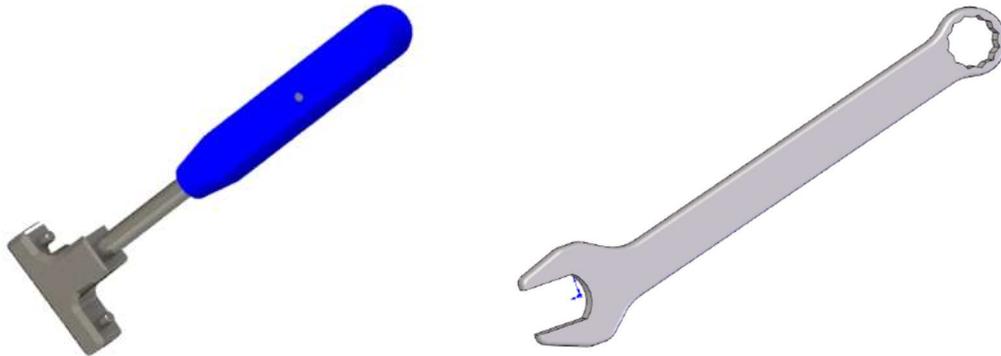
Tool zu RAP-hip Basisset (links), 11mm AF-Maul-/ Ringschlüssel (rechts)
